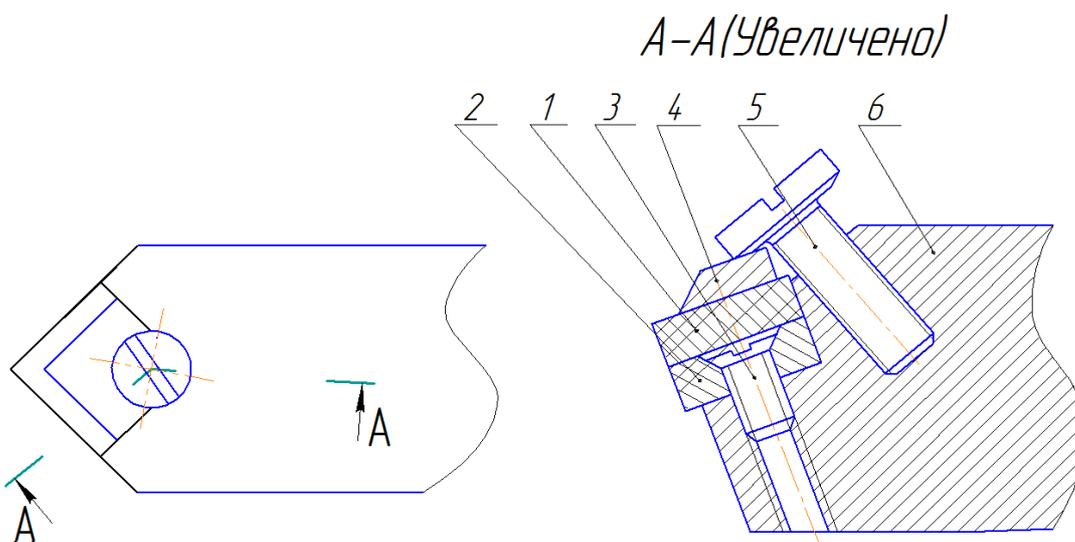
Способ крепления косым винтом минералокерамической пластины: 1 – режущая пластина; 2 – опорная пластина; 3 – винт опорной пластины; 4 – накладной стружколом; 5 – прижимной винт; 6 – державка
